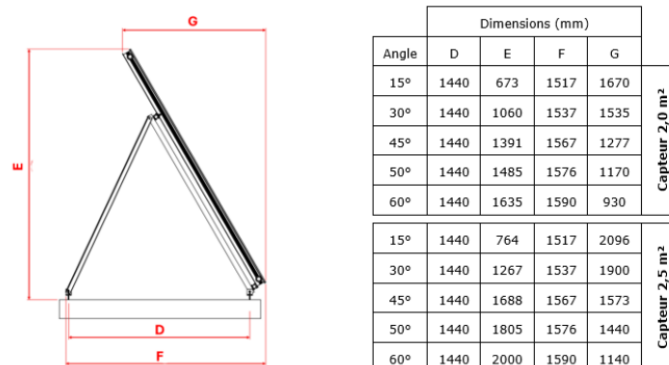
Dimensions des châssis (vue de côté) – Capteurs CEV et CMV
